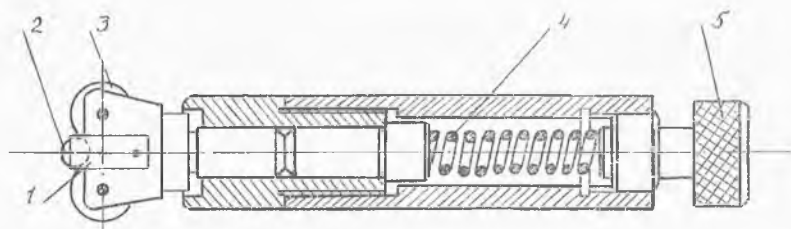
Конструкция шарикового обкатника: 1 — бронзовая скоба; 2 — шарик; 3 — подшипник; 4 — пружина; 5 — регулятор усилия обкатывания
